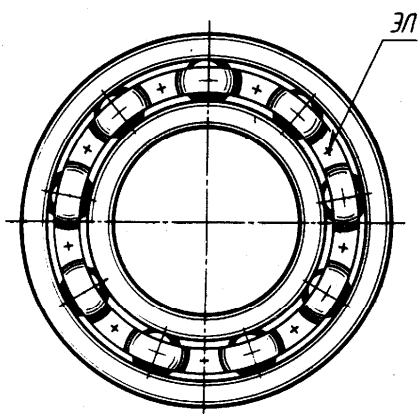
Шарикоподшипник с сепаратором, сваренный многолучевой сварочной установкой
